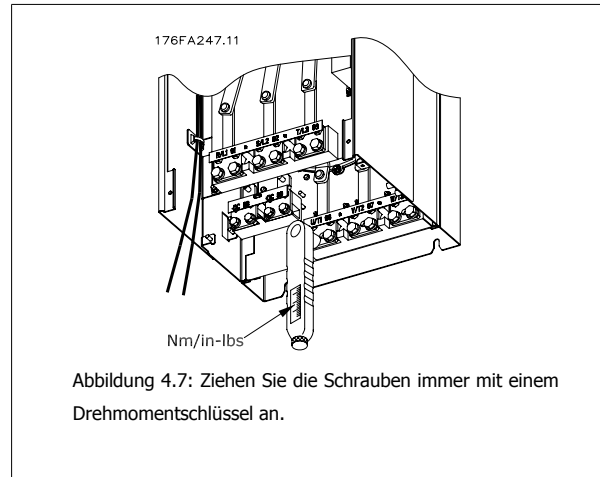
Ziehen Sie die Schrauben immer mit einem Drehmomentschlüssel an.
